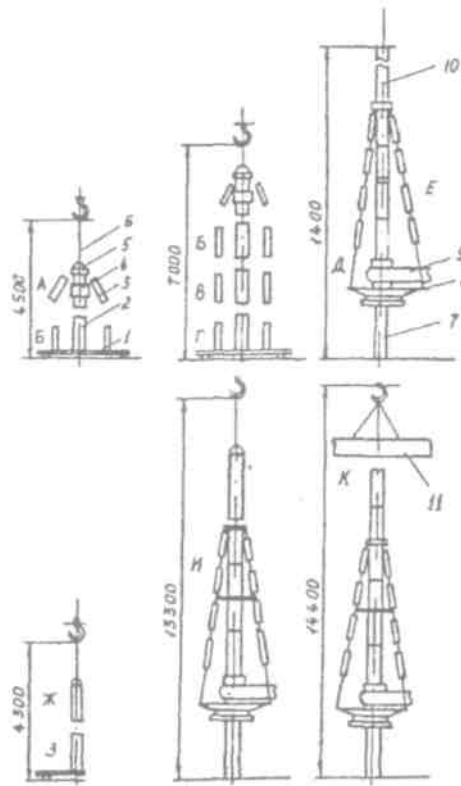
Сборка опорной колонки и установка дугогасительного устройства: А—К—последовательность сборки; 1 — настил из досок; 2 — опорный изолятор; 3 — изолятор растяжки; 4— жгут из ткани; 5— приспособление (поставляется заводом); 6 — строп 2СК-5.0 длиной 1500 мм; 7 — опорная стойка; 8 — рама; 9 — резервуар; 10 — нижняя стеклопластиковая труба; 11 — дугогасительное устройство
